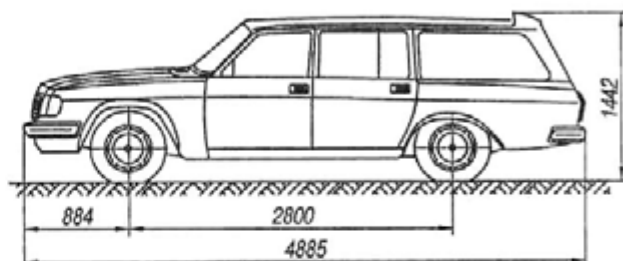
Автомобиль "Волга" ГАЗ-31022 и его габаритные размеры
